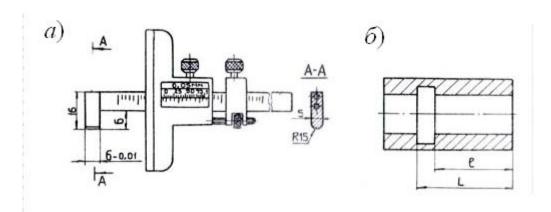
Общий вид штангенглубиномера со специальной планкой 1 (a) и эскиз канавки с измеряемыми размерами (δ)
